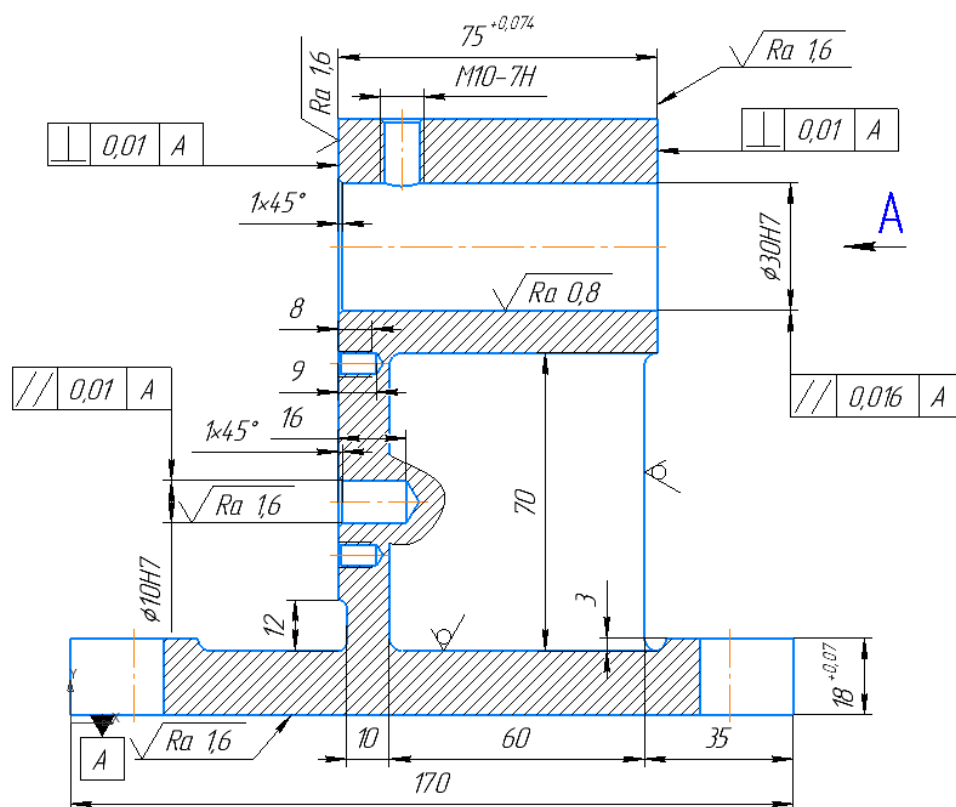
Чертеж детали 2 до метрологической экспертизы (главный вид)
